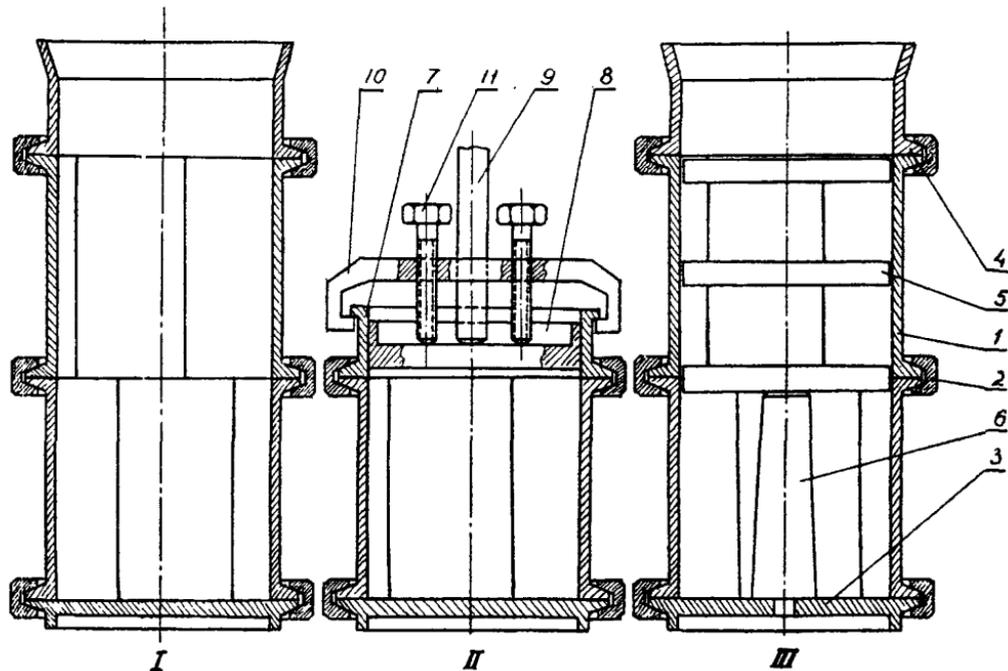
Сборные формы цилиндра: I - формообразующие сегменты; 2 - пояски крепления; 3 - днище; 4 - загрузочная воронка; 5 - перегородки; 6 - формователь осевого канала; 7 - силовая насадка; 8 - пресс-крышка; 9 - силовой шток; 10 - силовая скоба; 11 - прижимные болты. I - сборка для цилиндрических образцов размером  $\varnothing 15 \times 30$  см; II - сборка для цилиндрических образцов ускоренного твердения размером  $\varnothing 15 \times 15$  см; III - сборка для набора дисков размером  $\varnothing 15 \times 7$  см и цилиндров с осевым каналом.
